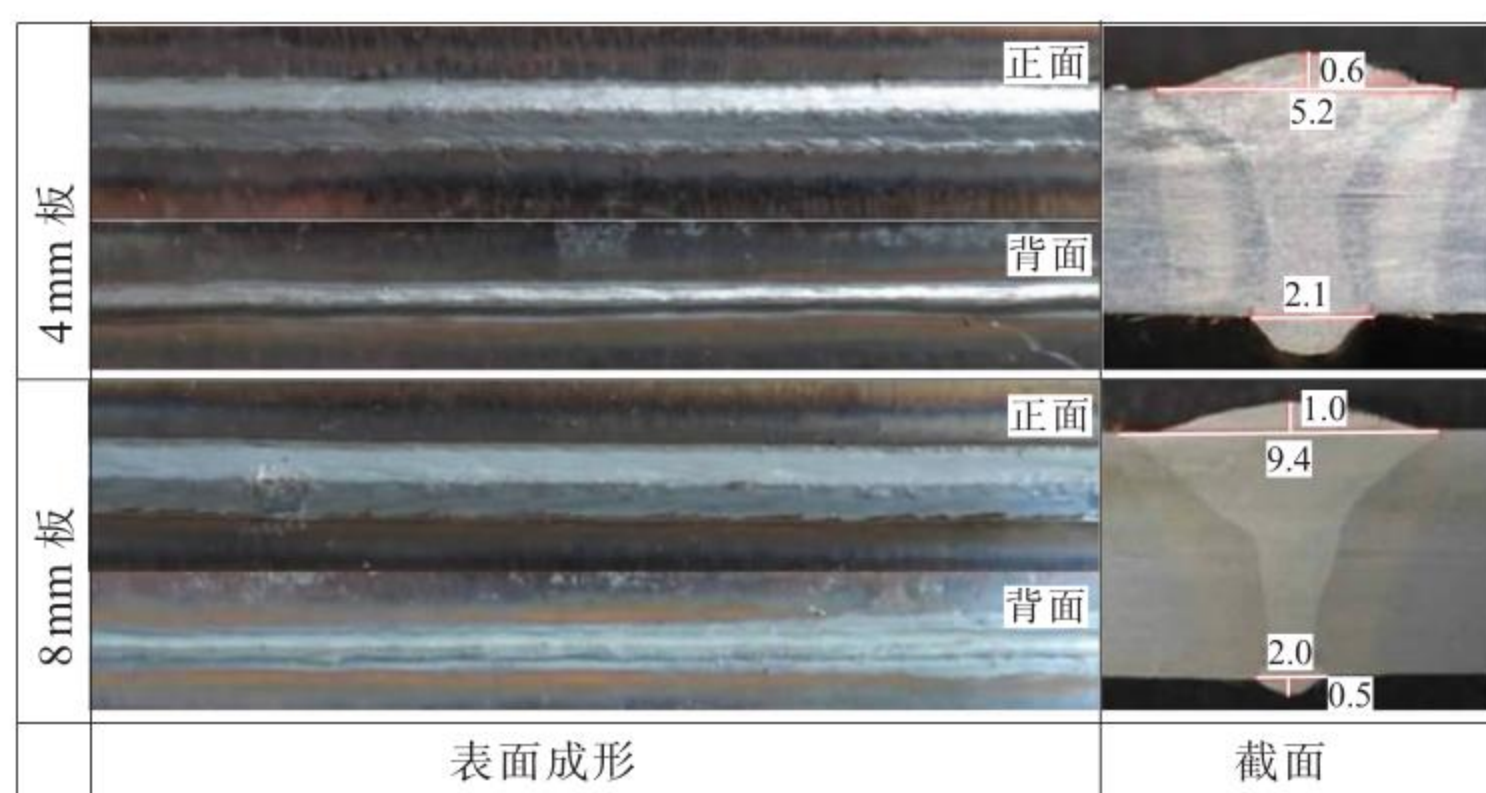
激光 -MAG 复合焊接头焊缝照片
